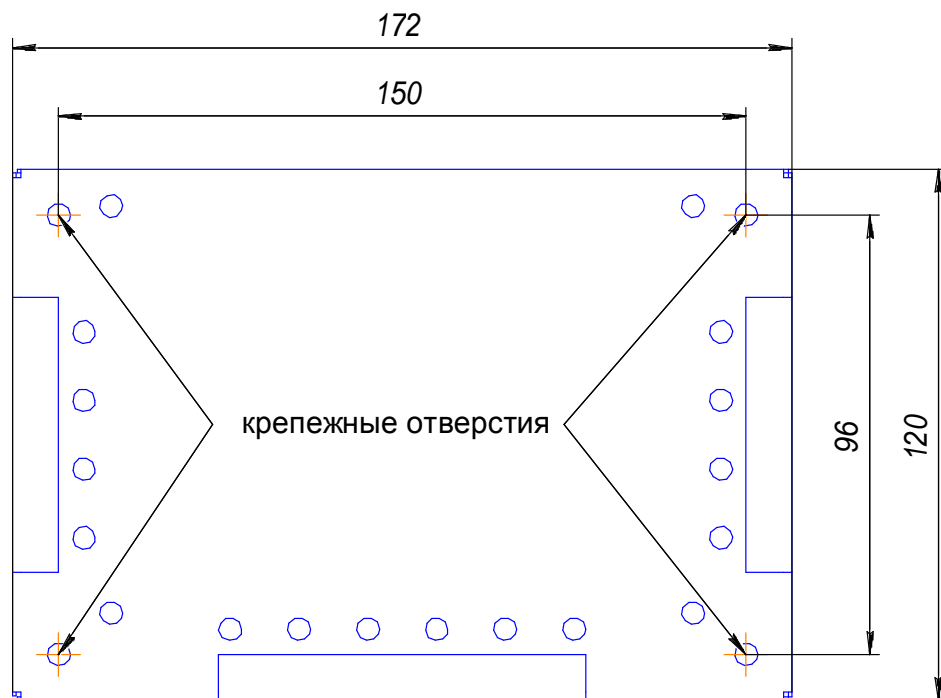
б. Разметка крепления АКШ ФИДШ.426461.001-01 в металлическом корпусе
